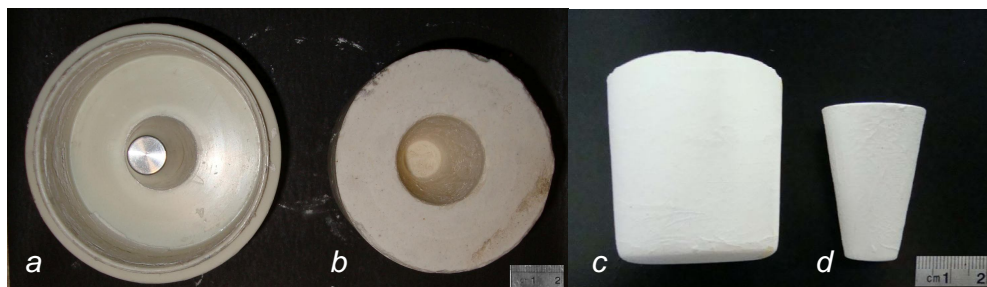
(a) modelo para molde de gesso; (b) molde de gesso; (c) cadinho e (d) molde para fundição.
